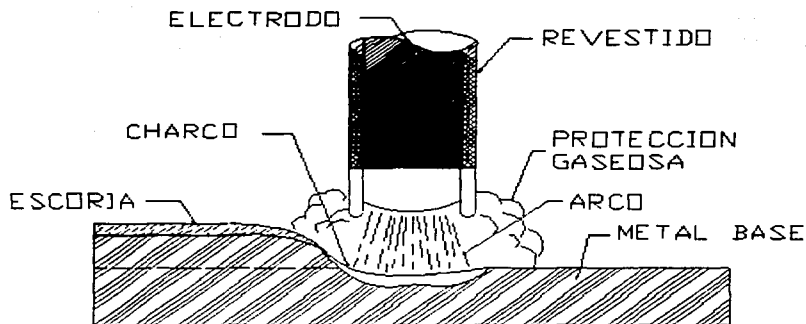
Soldadura de Arco Metálico Protegido
